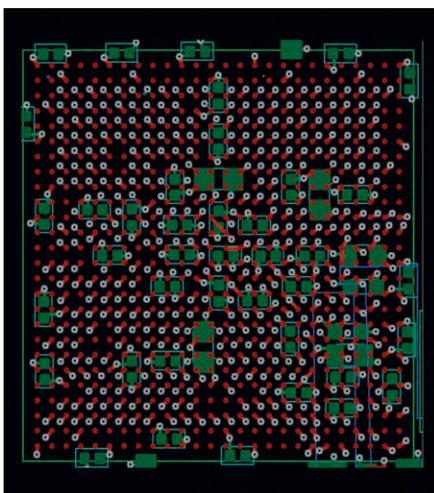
Расстановка фанатов для BGA с двухполюсниками с обратной стороны платы
